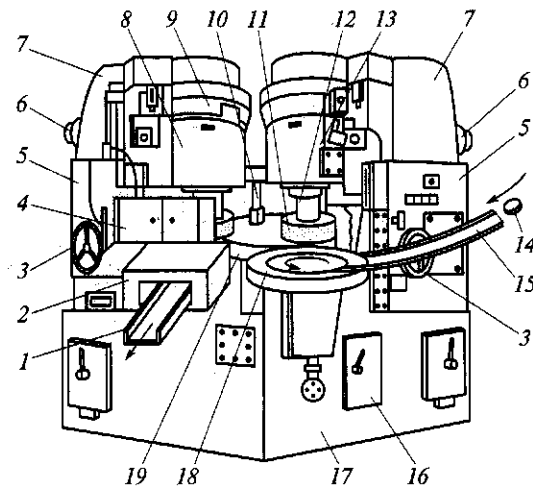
Двухшпindelный плоскошлифовальный станок с круглым столом:
